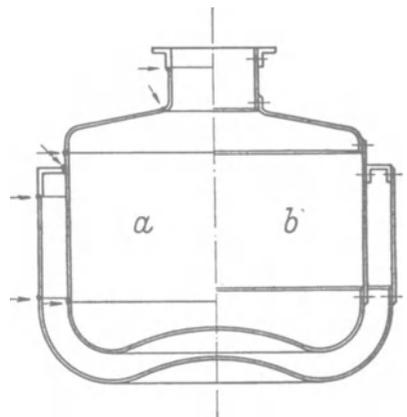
Kochkessel, geschweißt und genietet.
